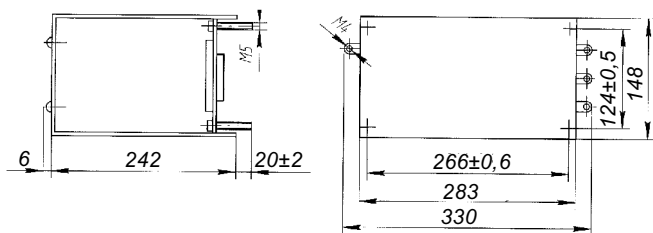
Габаритные, установочные размеры блока типа БЭ 1105.
